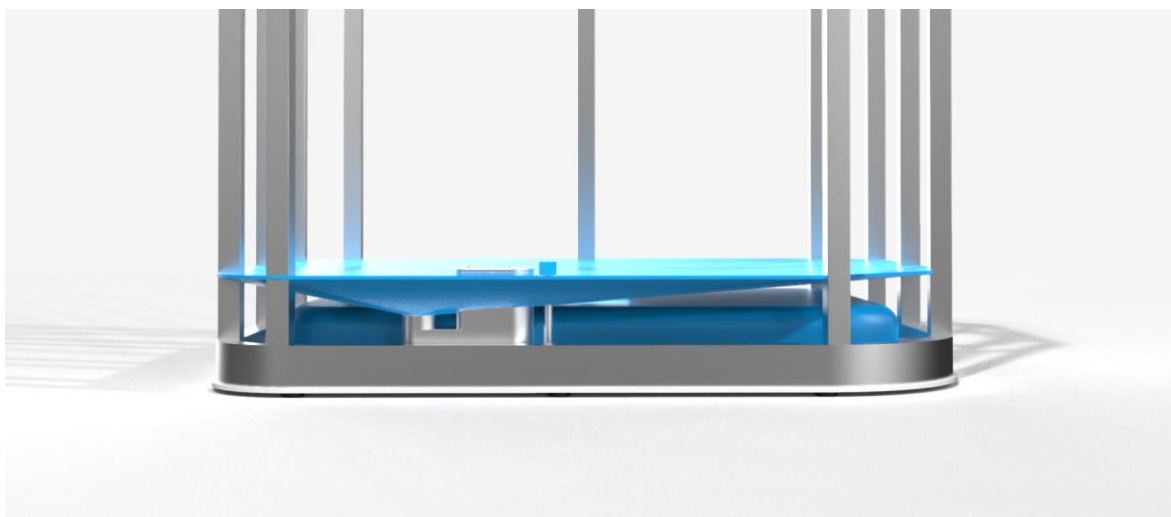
11 Pohled 3/4 přední a zadní – rám stroje
